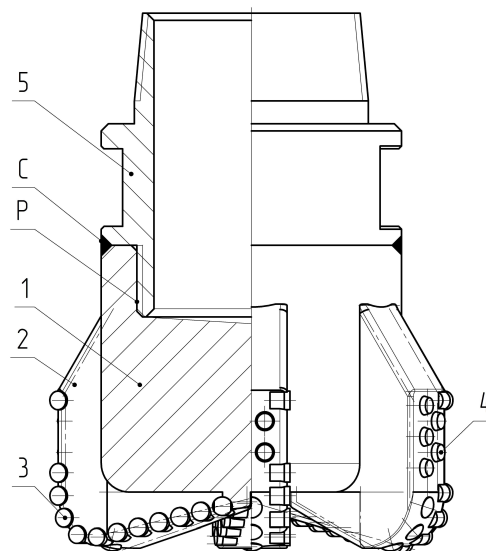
Алмазное долото: 1 – корпус долота; 2 – лопасти; 3 – режущие зубки с алмазоносным слоем; 4 – резцы защитного действия; 5 – ниппель; P – резьбовое соединение; C – сварочный шов
